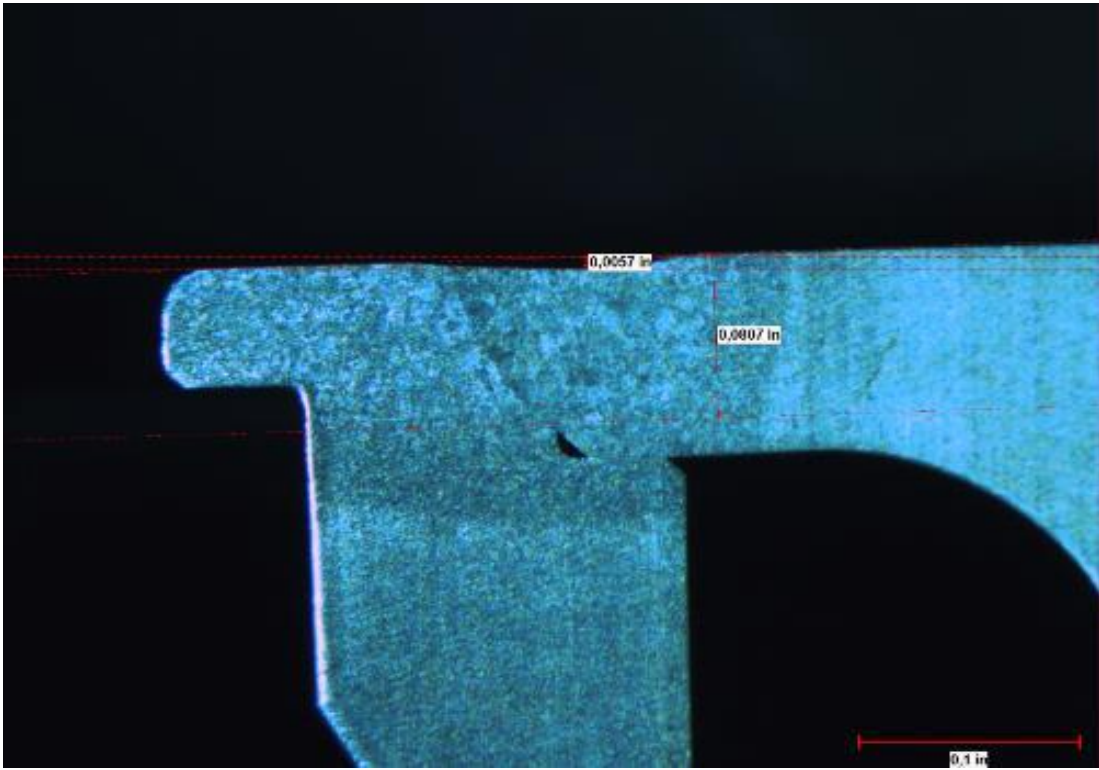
Kupon 3 kesiti makro görüntü (KN: 1.90, KYÇ: 0.18) / Kaynak bölgesi 2
